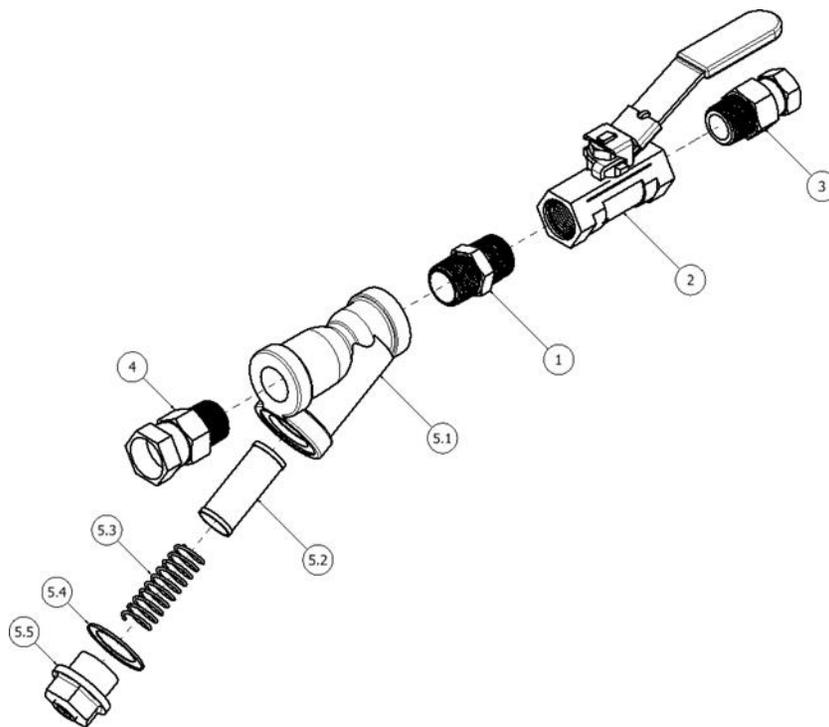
Ensamblaje del filtro en Y, lado "A"
